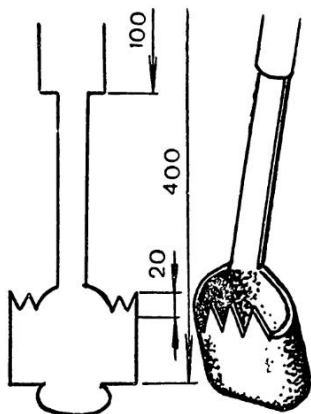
Ковш-черпак для сбора крыжовника (общий вид и развертка)
